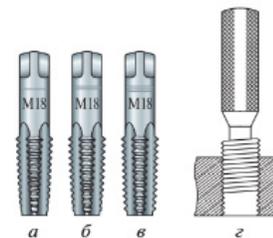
Комплект из трёх метчиков: а — черновой; б — средний; в — чистовой; г — резьбовой калибр
